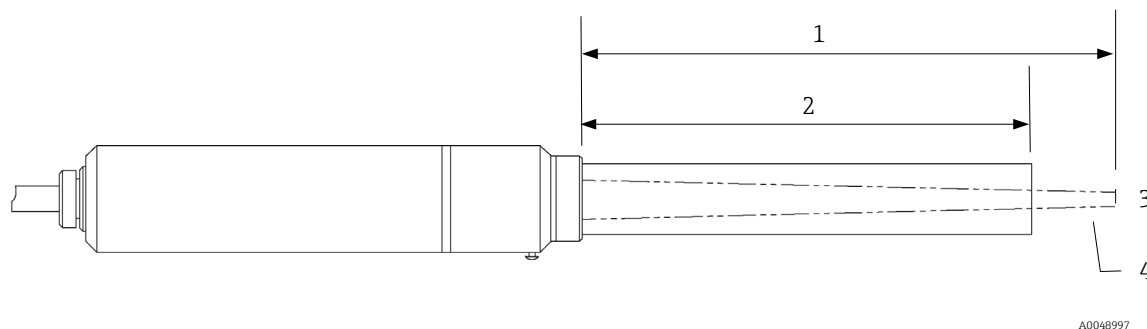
Sonde Rxn-20 avec adaptateur de lentille et tube de lentille non purgeable
